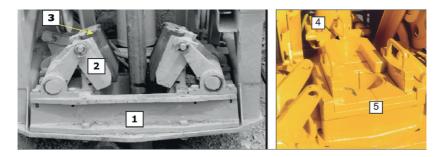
Зажим штанги: 1 – зажим штанги в сборе; 2 – держатели губок; 3 – губка штанги (различных размеров); 4 – механизированный гаечный ключ; 5 – стол для плашек для захвата бурильных труб
